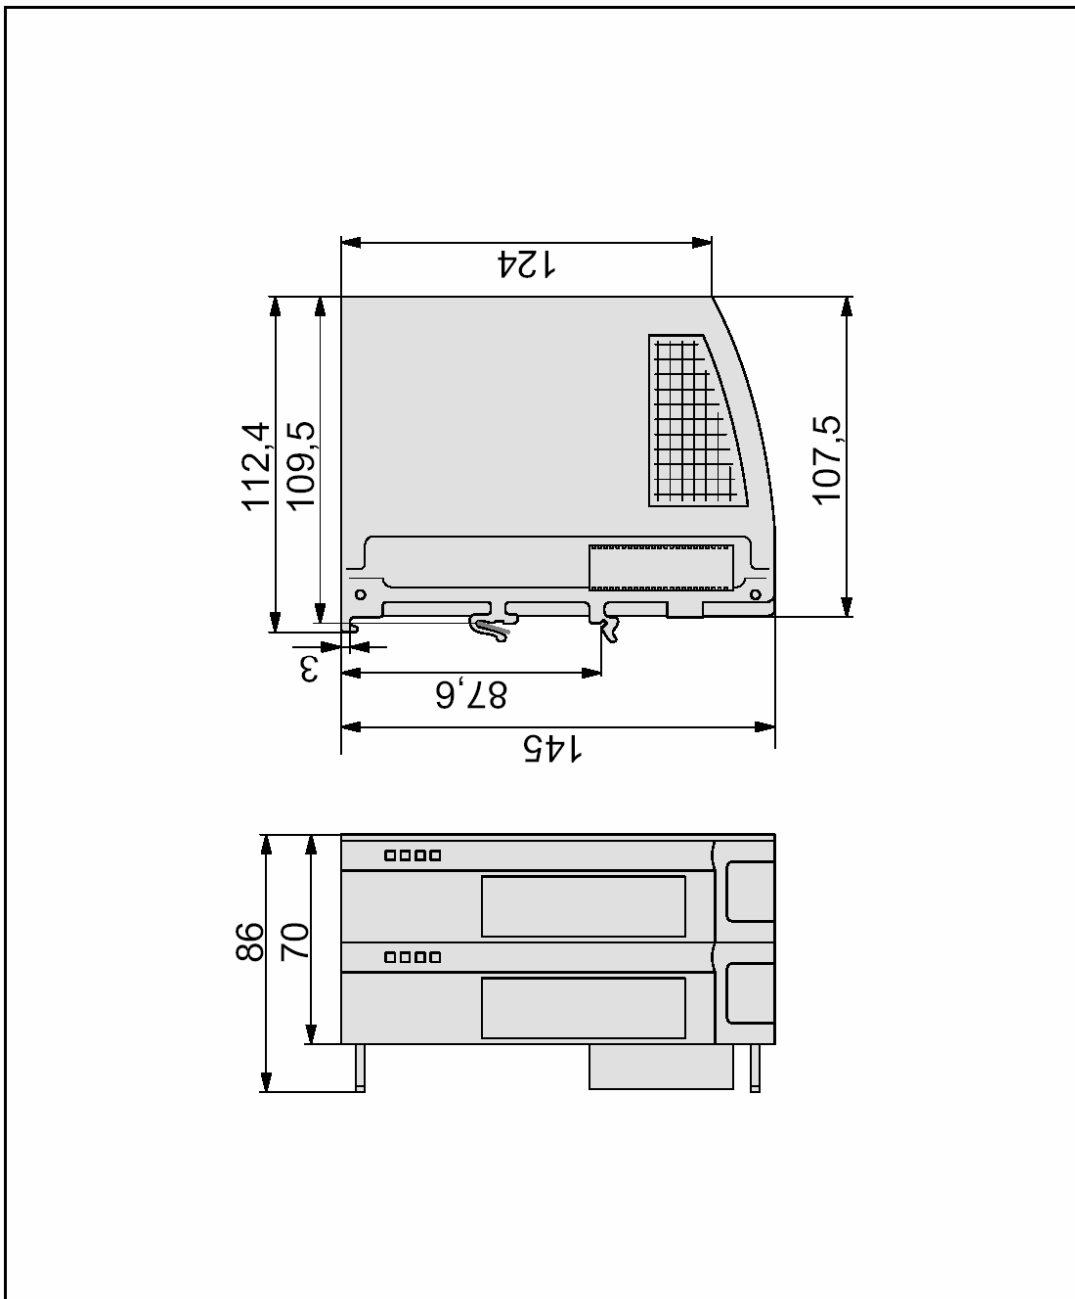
Габаритные размеры модуля расширения EM495-8
